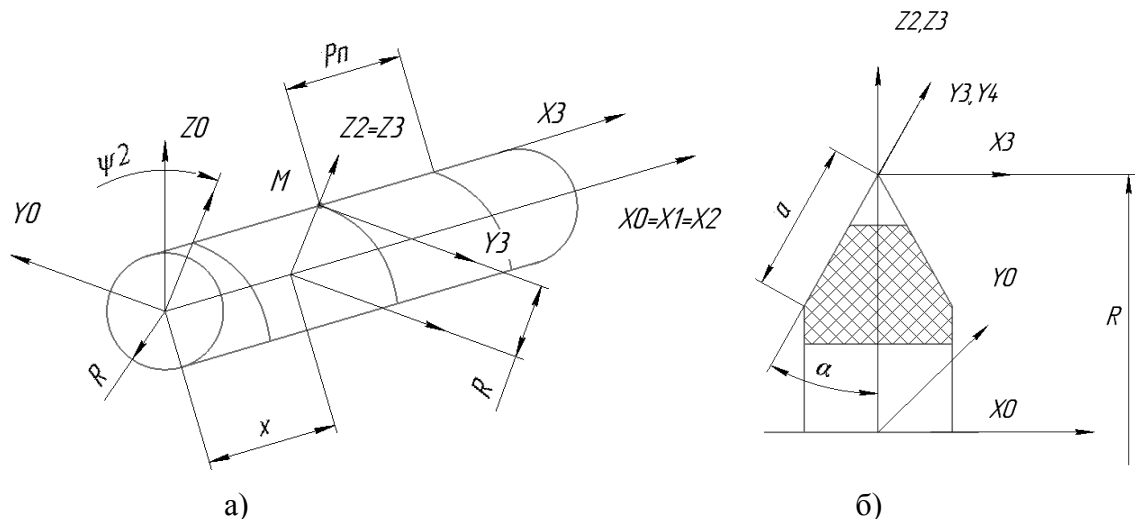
Геометрична модель черв'ячного інструменту: а) схема черв'яка; б) профіль черв'яка
